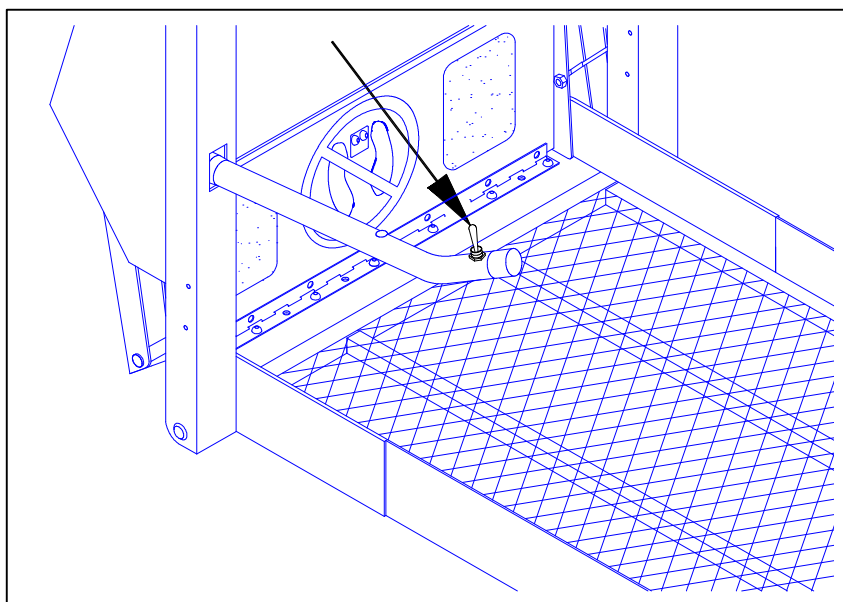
COMMANDE MONTÉE SUR LA RAMPE
